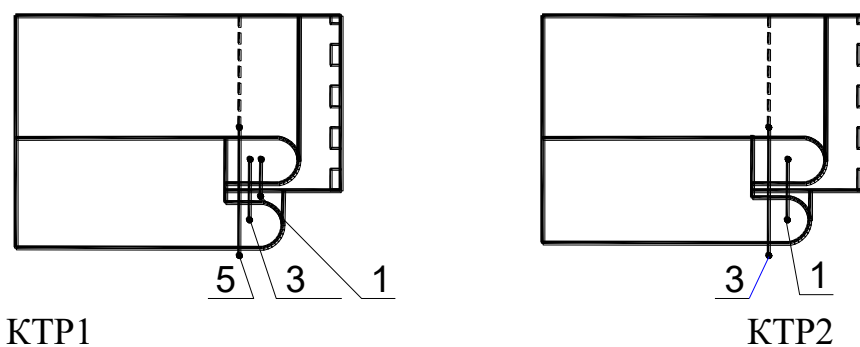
Багатоваріантна обробка краю борта плаща
